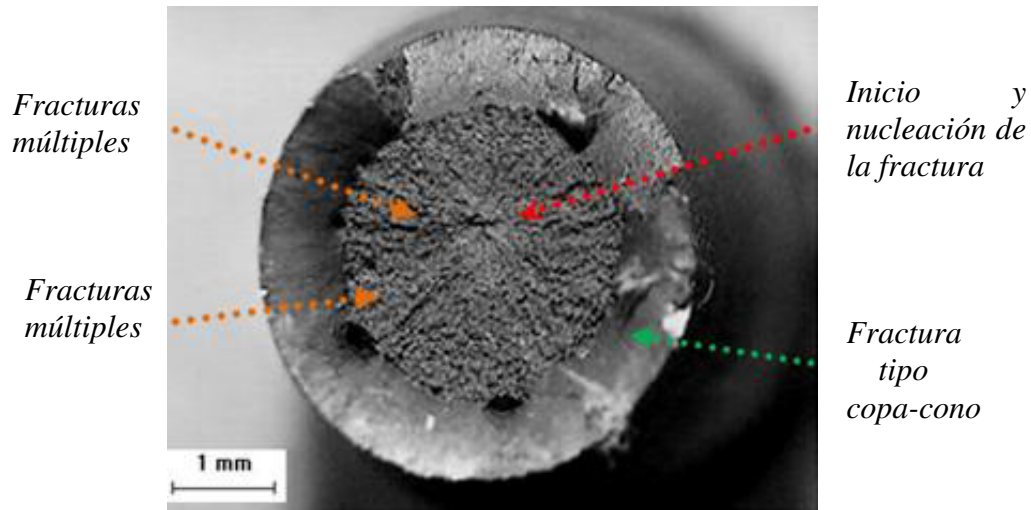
Macrografía de la probeta 10, tipo de fractura dúctil
